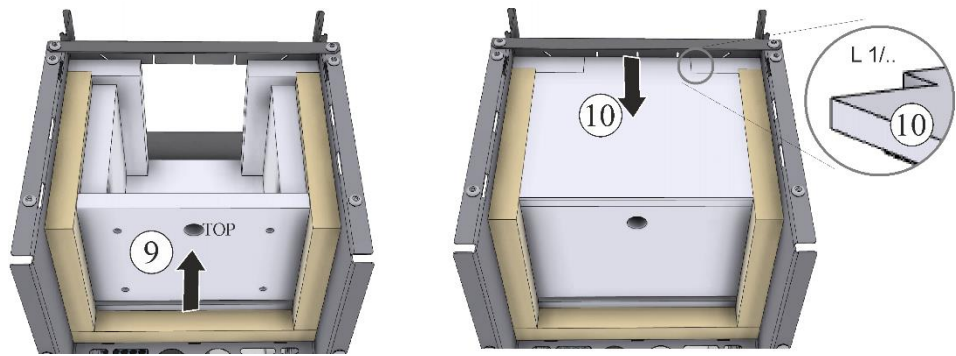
Montaje del aislamiento de la pared posterior y del techo (figura análoga)
